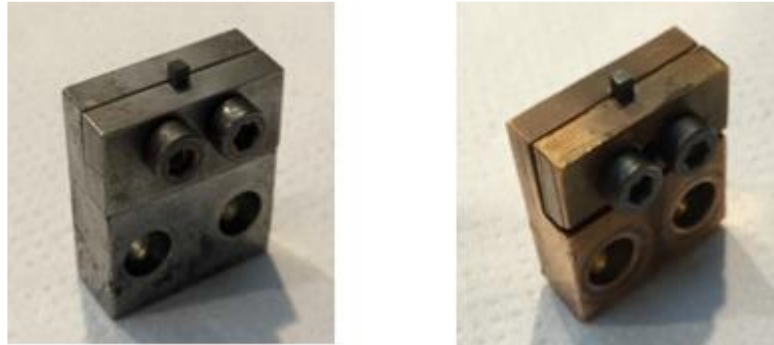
Soportes del diamante, acero (izquierda) cobre (derecha).
